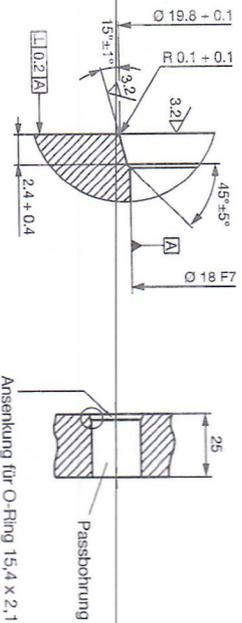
Passbohrung für die Montage des BTL mit O-Ring
